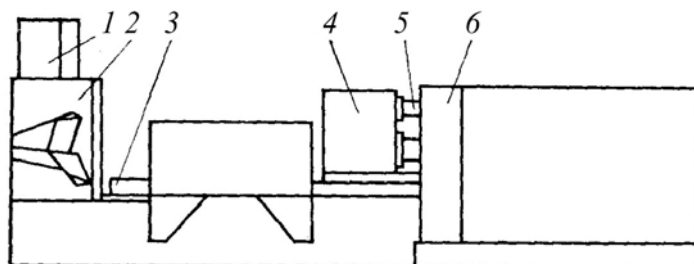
Гидравлический древокольный станок КГ-8А
